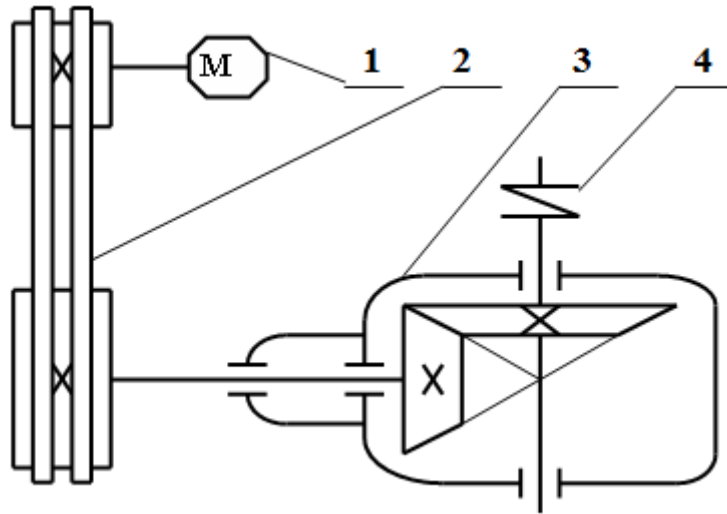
Привод інерційного конвеєра: 1 – електричний двигун, 2 – пасова передача, 3 – одноступінчатий прямозубий конічний редуктор, 4 – муфта типу МПВП.
